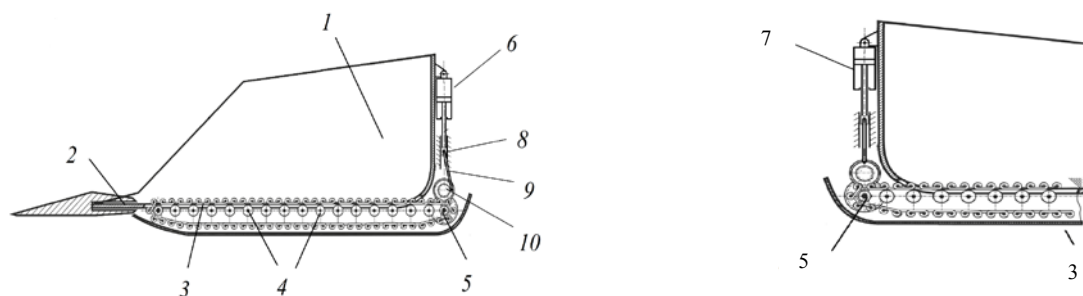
Ковшовый рабочий орган с конвейерным днищем в виде замкнутой ленты, связанной передаточными механизмами с приводом из двух гидроцилиндров: 1 — боковая стенка; 2 — конвейерное днище; 3 — лента; 4 — поддерживающие ролики; 5 — ведущий ролик; 6, 7 — гидроцилиндры; 8 — ползуны; 9 — шатуны; 10 — кривошипы
